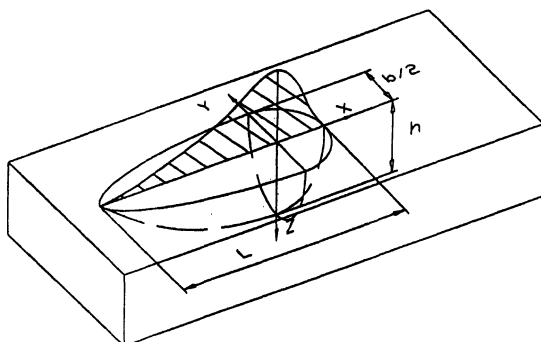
Схема сварочной ванны и расположение координатных осей
